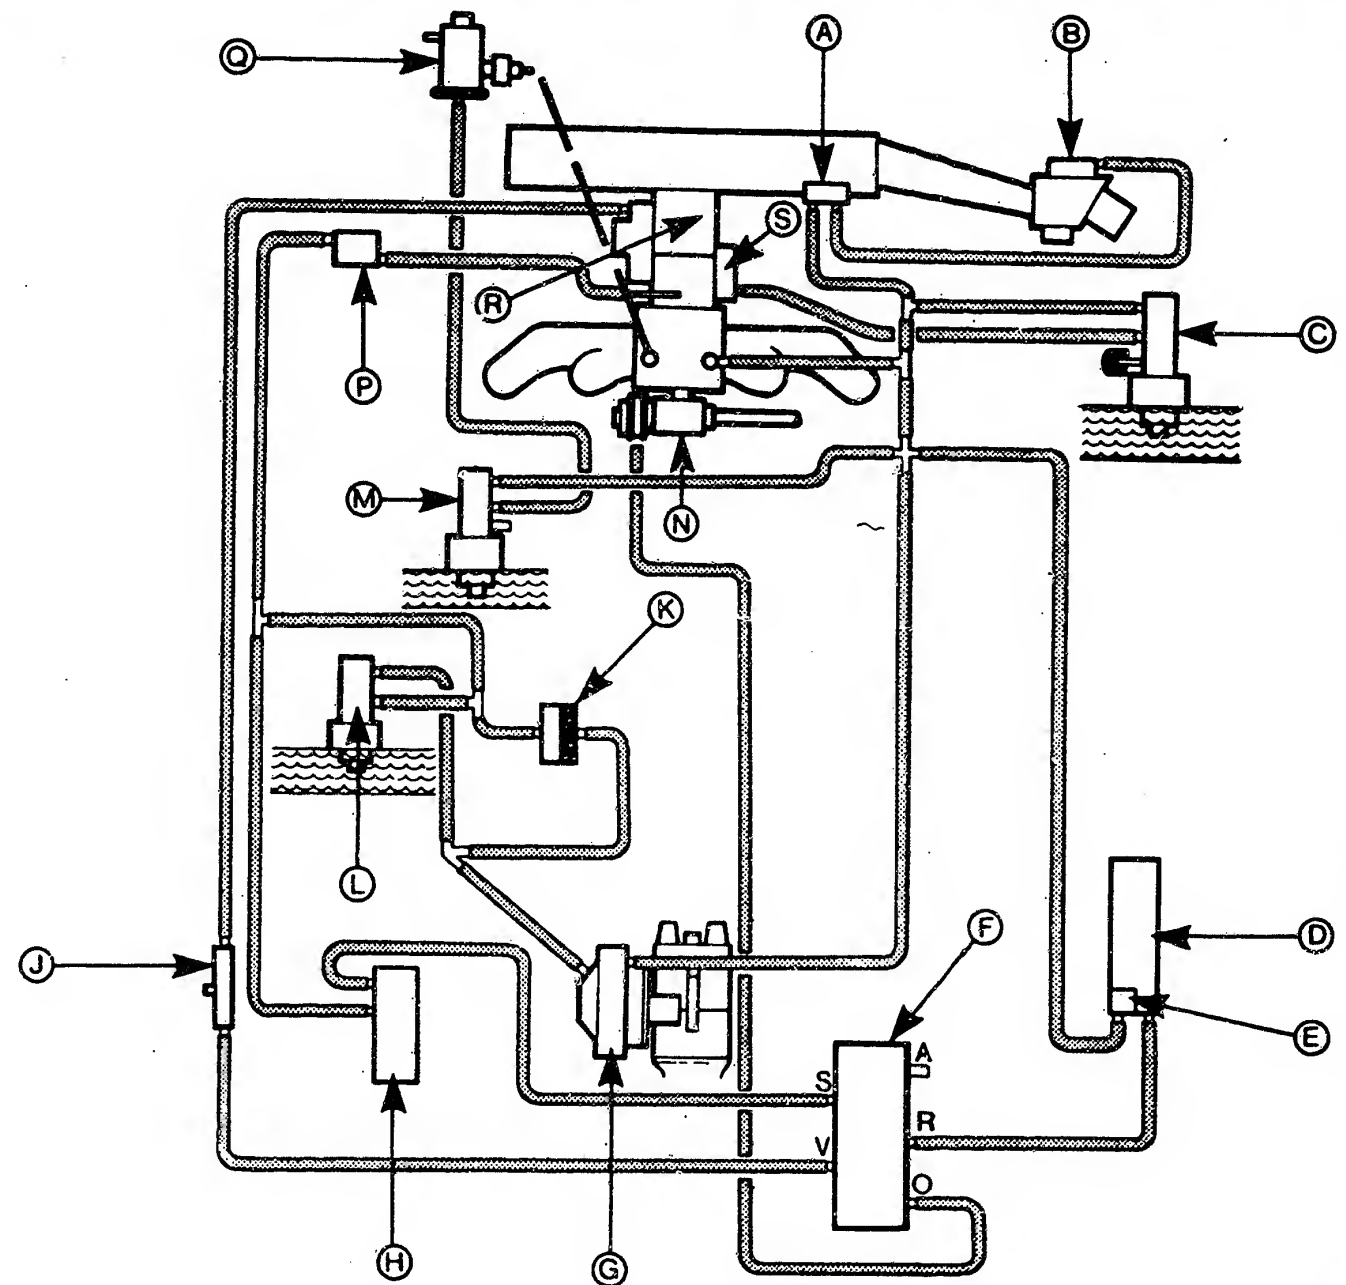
Abgasentgiftungsanlage für die Version mit Handschaltgetriebe. Bei Fahrzeugen mit Getriebeautomaten entfällt das Verzögerungsventil: A Bimetallventil – B Unterdruckdose – C Dreikanal-Unterdruckthermostat – D Rückschlagventil, Vakuumbehälter – F Unterdruckverstärker – G Doppelmembran-Zündverteiler – H Zweikanal-Unterdruckthermostat (Abschalter EGR-Ventil) – J Drossel, Belüftung – K Ventil, Frühzündungsunterstützung – L Zweikanal-Unterdruckthermostat (Spätzündung) – M Dreikanal-Unterdruckthermostat (Abschalter Verzögerungsventil) – N EGR-Ventil – P Gemischregulator – Q Verzögerungsventil – R Weber-(2V)-Vergaser – S Unterdruckericherungs-Vorrichtung.
